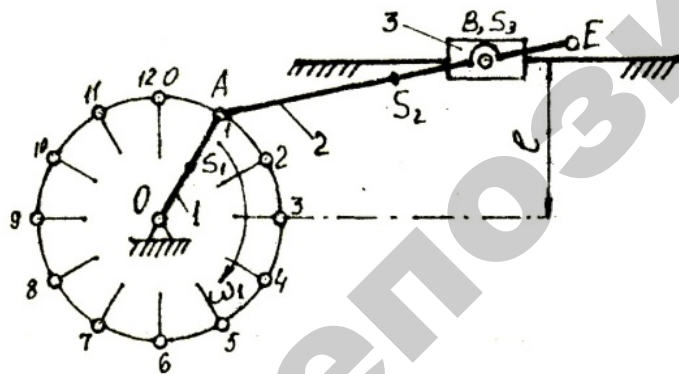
Схема 8 кривошипно-ползунного механизма
